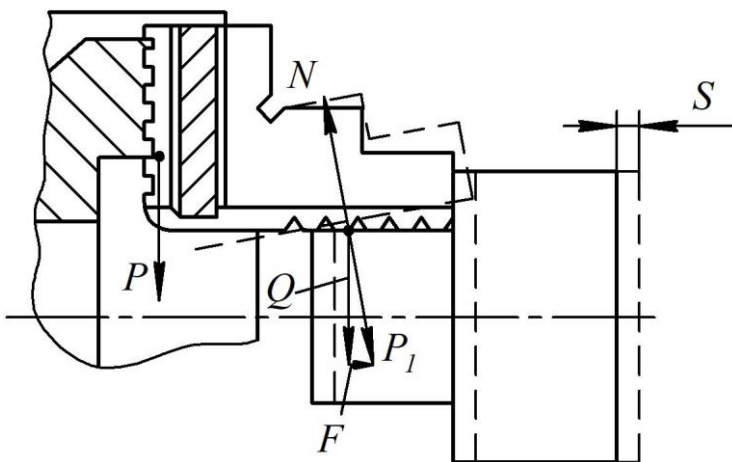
Схема сил, що діють на заготовку під час її закріплення в токарному патроні
